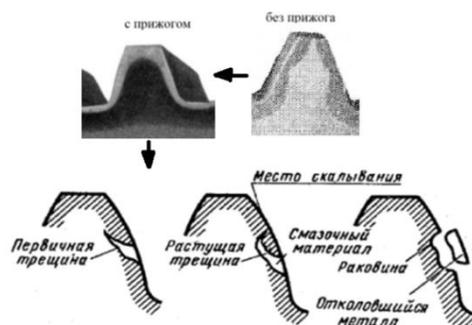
Прожоги зубчатых колес до и после химико-термической обработки или шлифование зубчатых колес, при котором возникают трещины на детали
